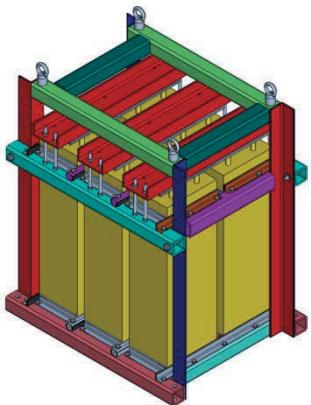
Внешний вид устройства СА-У.
